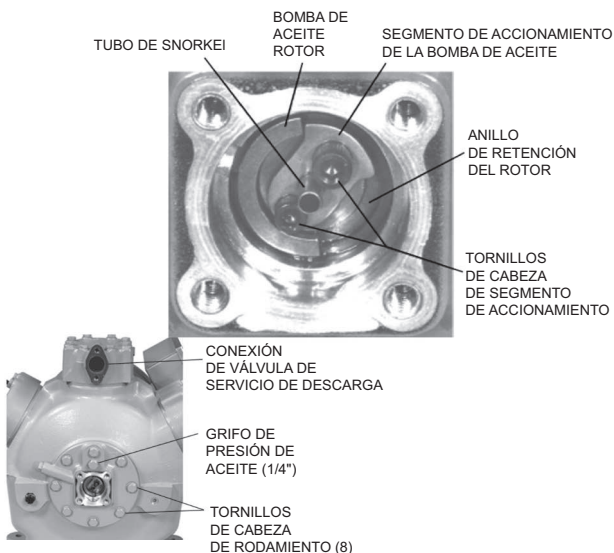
Extracción del cabezal del cojinete del extremo de la bomba (Compresor 06D)
